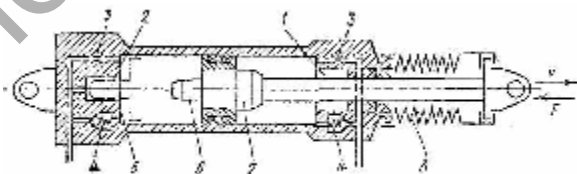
Схема гидроцилиндра с концевыми дроссельными тормозами и защищенным штоком:
